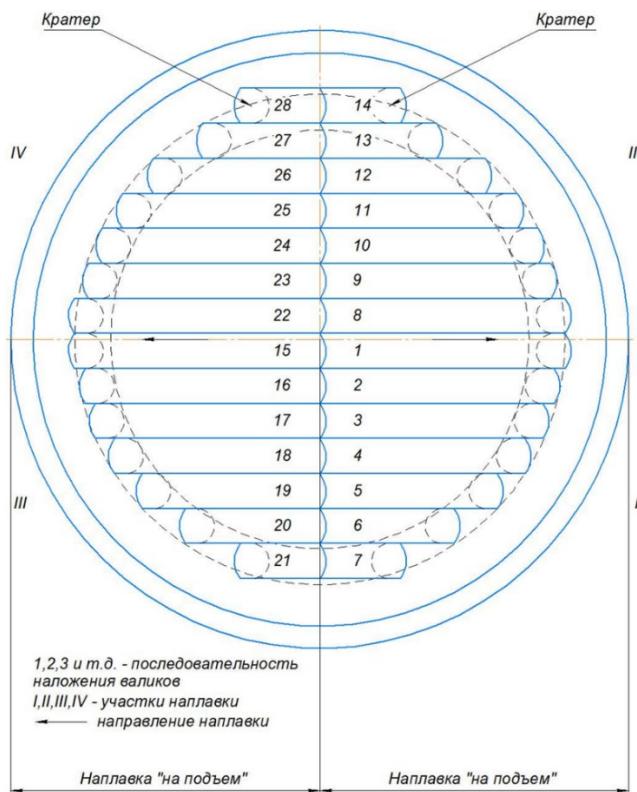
Схема наплавки центра внутренней поверхности днища ёмкости
